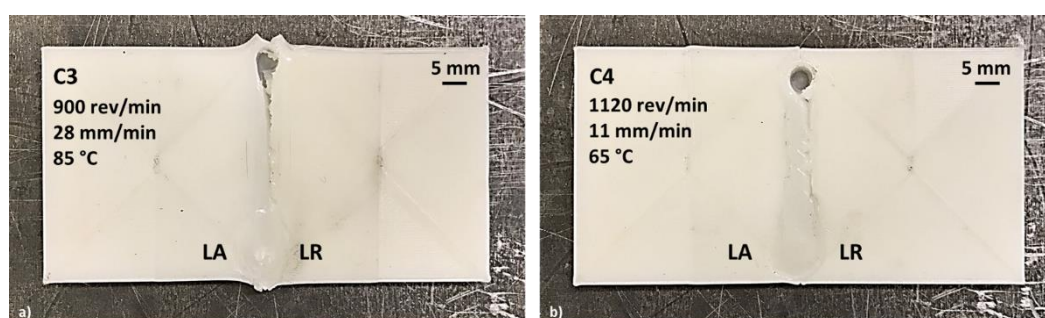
Aspeto visual da superfície das placas soldadas com combinação de parâmetros 3 e 4.
